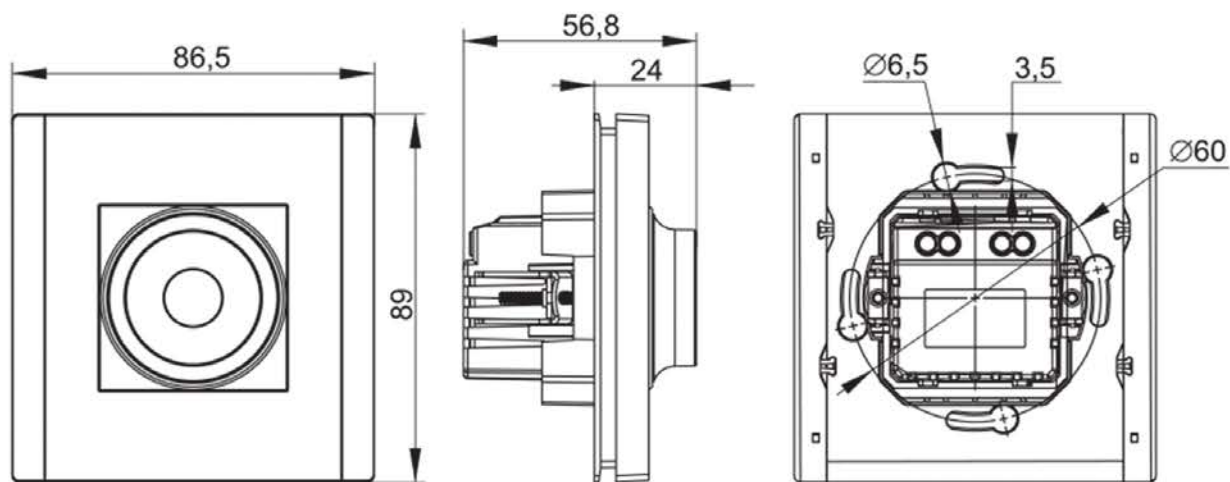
Габаритные и установочные размеры диммера / Figure 2 – Overall and installation dimensions of the dimmer / 2 сурет – Диммердің габариттік және орнату өлшемдері / Figura 2 – Dimensiunile generale și de instalare ale variatorului / 2-rasm – Dimmerning gabaritlari bo'yicha hamda o'rnatilishdagi o'lchamlari
